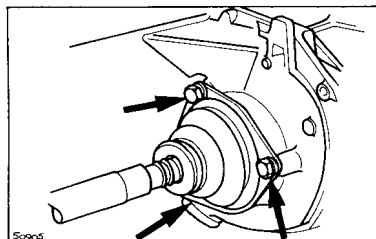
Болты крепления шарнира вала привода левого колеса
